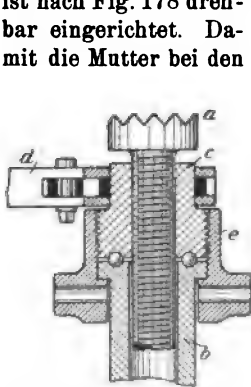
Kopf einer Bohrsäule mit drehbarer Mutter.
